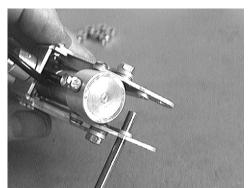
zeigt die montierte Schraube. Achtung!! Die Schrauben dürfen nur ganz leicht angezogen werden 'da sonst der Zylinder beschädigt wird.Bitte Schraubensicherungslack verwenden.
